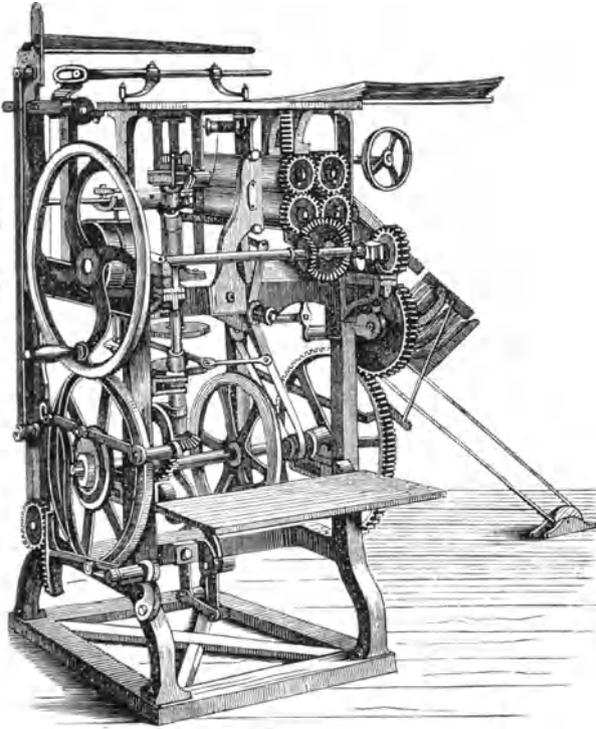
Frauentfelder Falz- und Heftmaschine.
